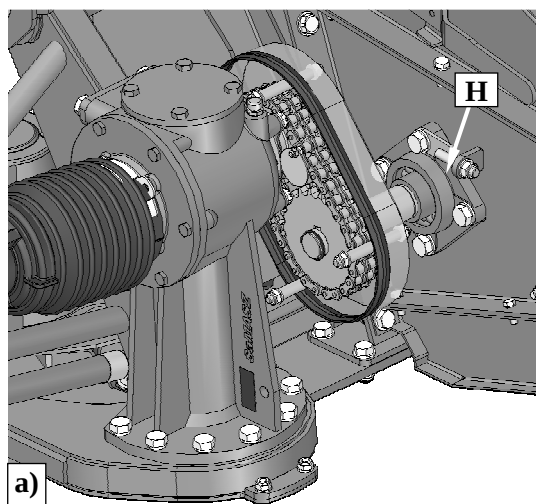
Регулировка напряжения цепи цепной передачи (вид без части защиты):
